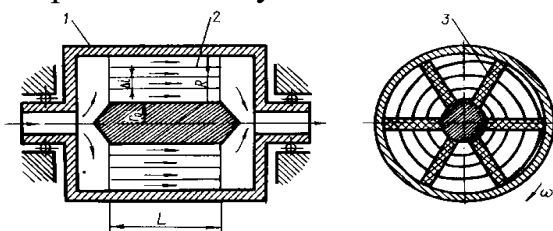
Схема тонкошарової центрифуги з однокамерною спіральною вставкою: 1 - корпус ротора; 2 - спіральна вставка; 3 – прокладка
